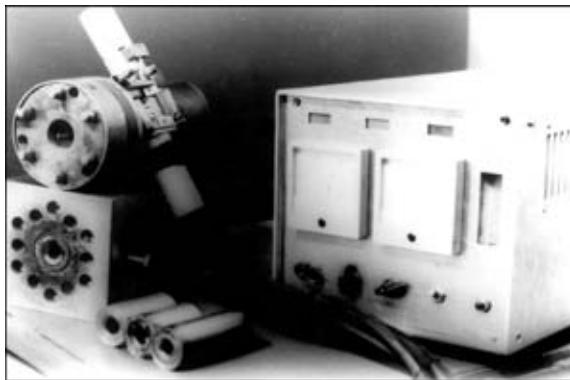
Сварочный автомат «Комета-М» для сварки труб с трубными решетками погруженной дугой
